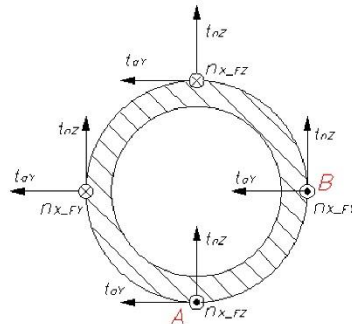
Esfuerzos actuantes en cordón de soldadura
